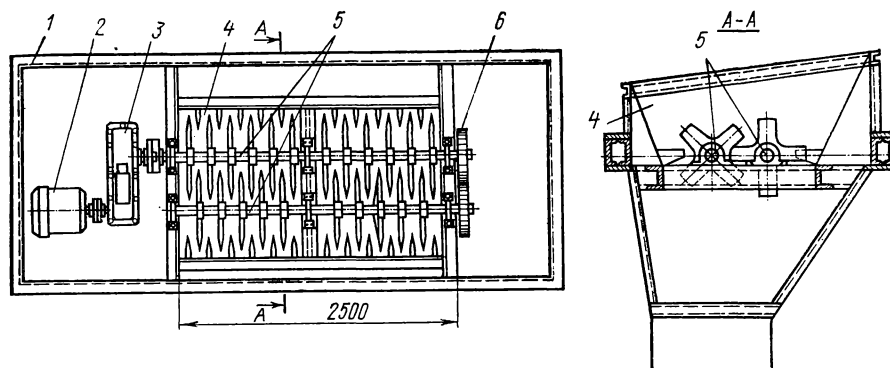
Двухвальный глинорыхлитель конструкции Ленстройкерамики:
